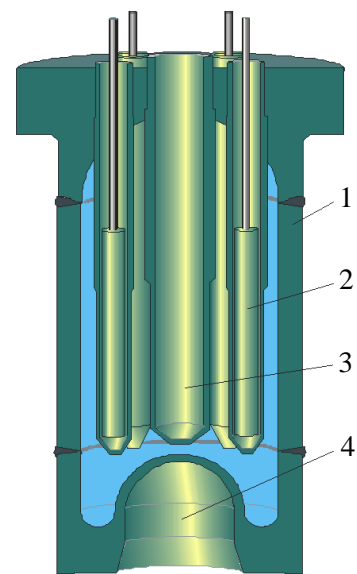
Вертикальный разрез корпуса АЗ реактора ВИР-2М: 1 – корпус АЗ; 2 – СУР (6 шт.); 3 – ЦК; 4 – ПСК
